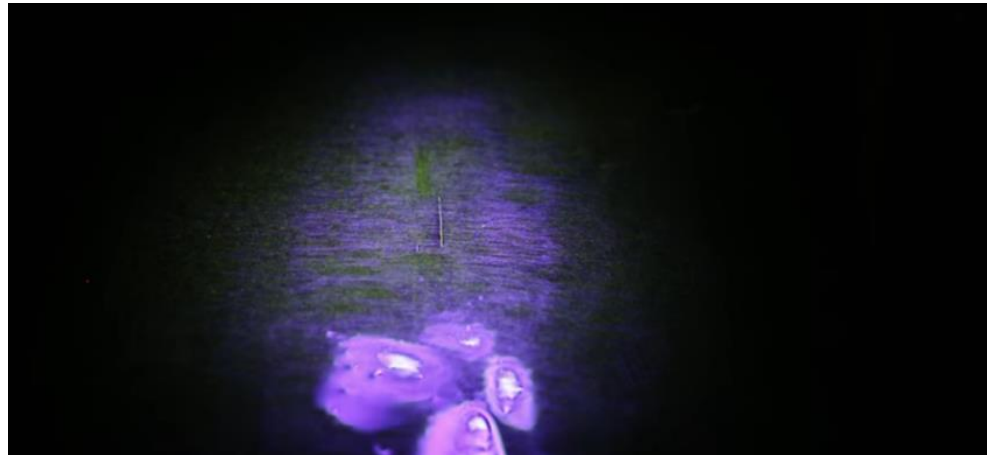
Hallazgo de discontinuidades en la superficie de la junta soldada [11].
